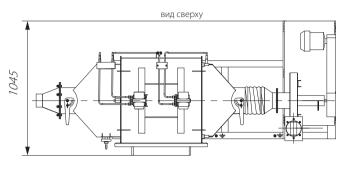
Общий вид установки УФАПЭ-500 РЕ 725.00.00.000.
